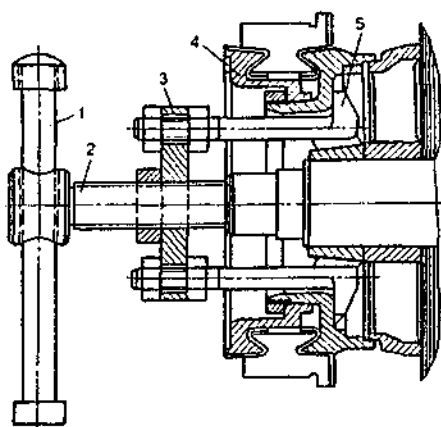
Приспособление для снятия коллектора с вала якоря
